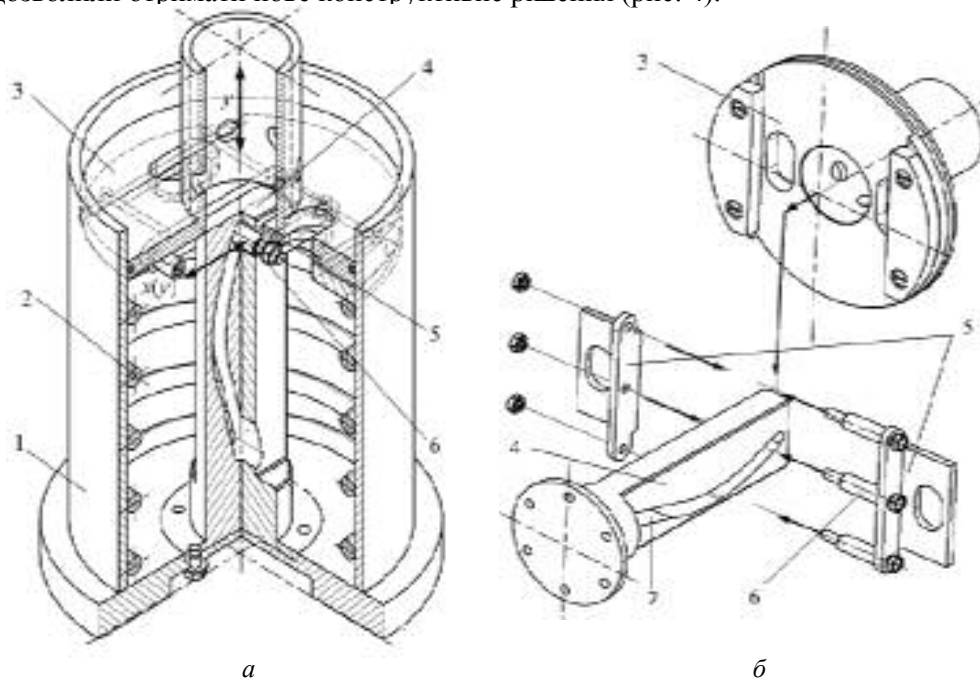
Пасивний реласакційний амортизатор з нелінійним механічним зворотним зв'язком: загальний вигляд (а); схема складання елементів зворотного зв'язку (б)
